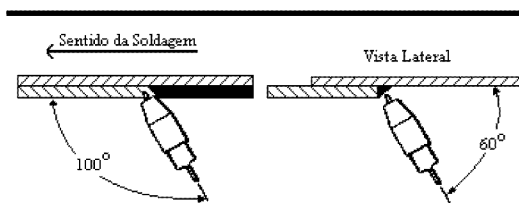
Soldagem TIG de Junta Sobreposta na Posição Sobrecabeça.
